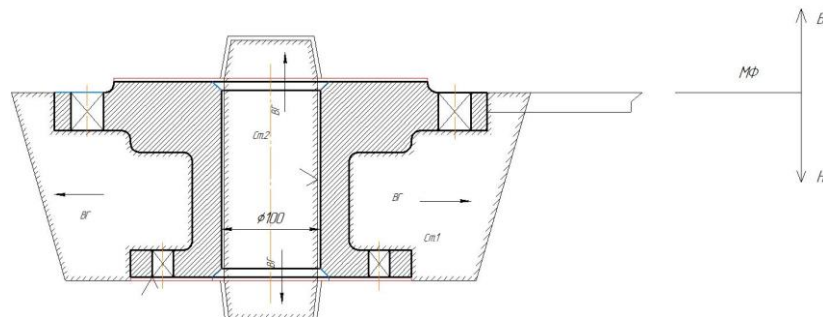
Вибір положення виливка в ливарній формі
